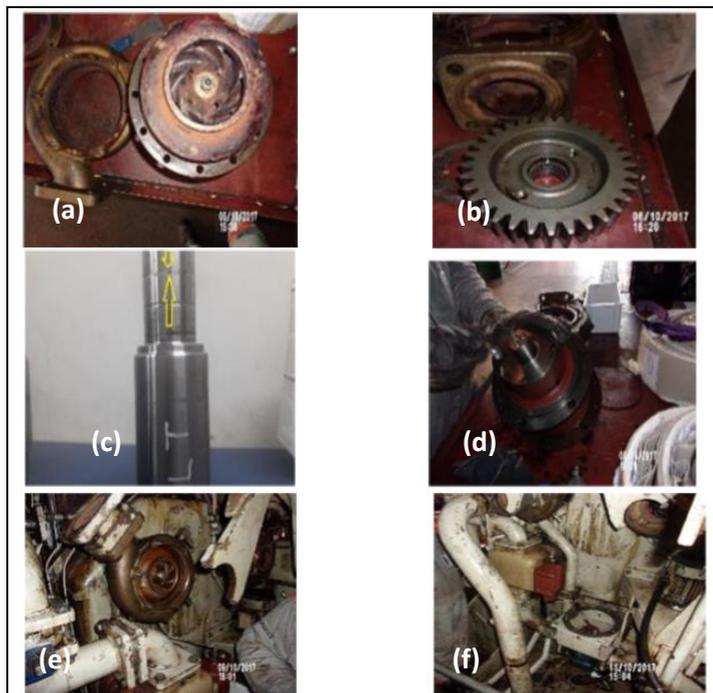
(a) Desmontagem; (b) Inspeção; (c) Eixo com desgaste na área do retentor; (d) Revisão da bomba; (e) Montagem da bomba; (f) Instalação e torque das tubulações de LT.
